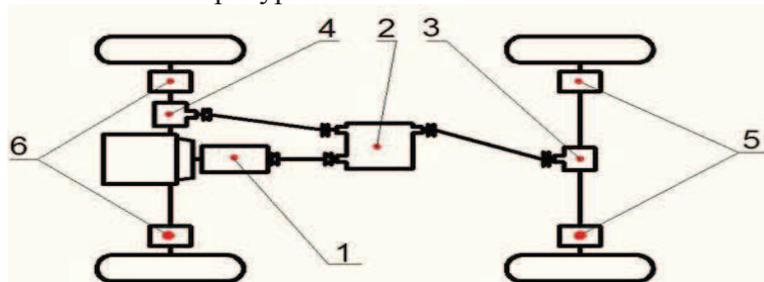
Схема привода колес ТСШСД ТРЭКОЛ-39041
